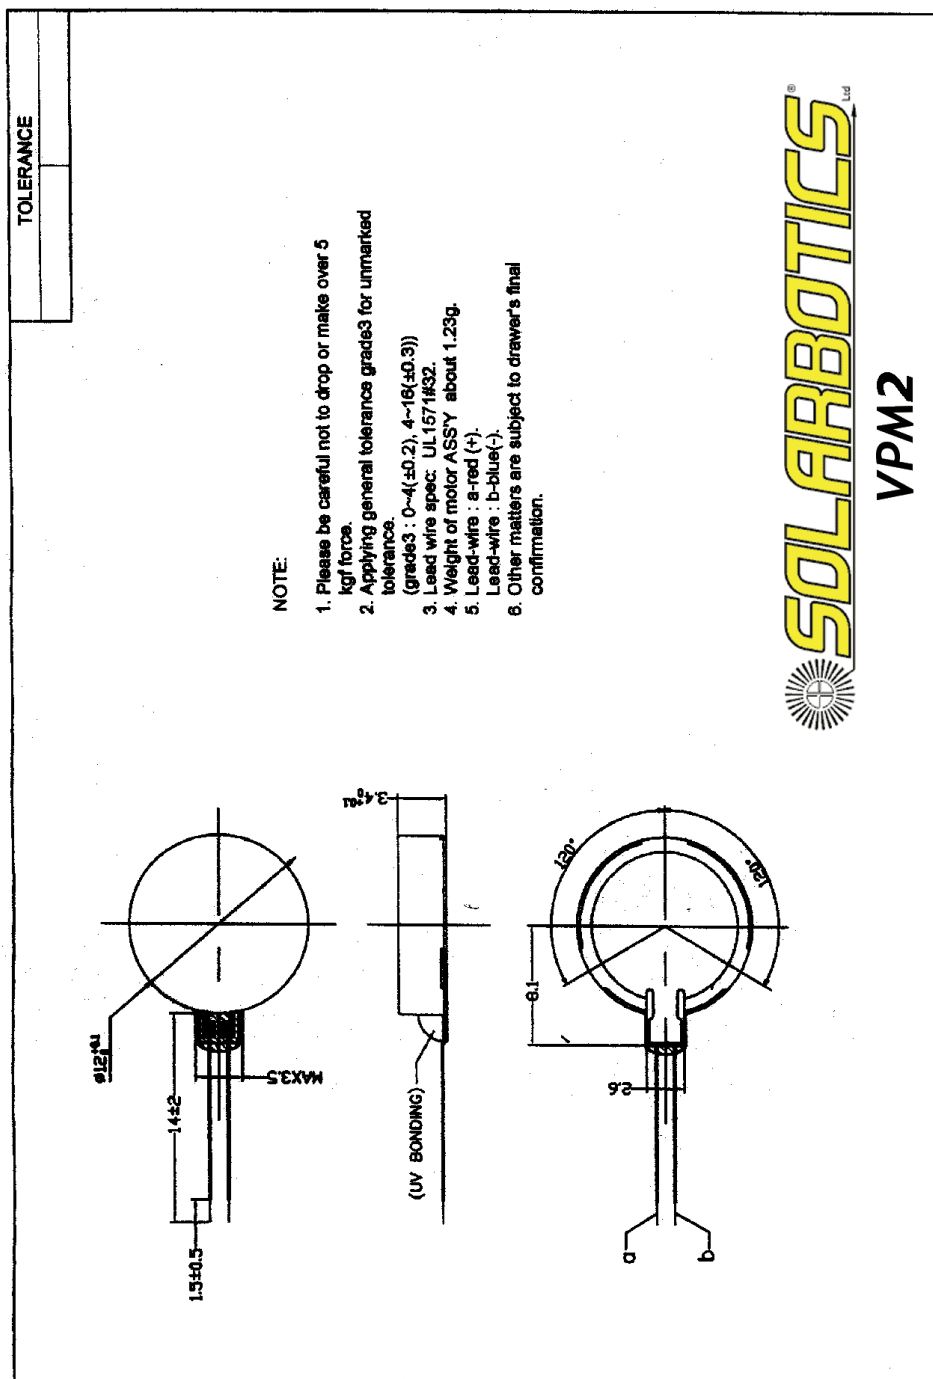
dimensiones actuador - Cortesía de Solarbotics
